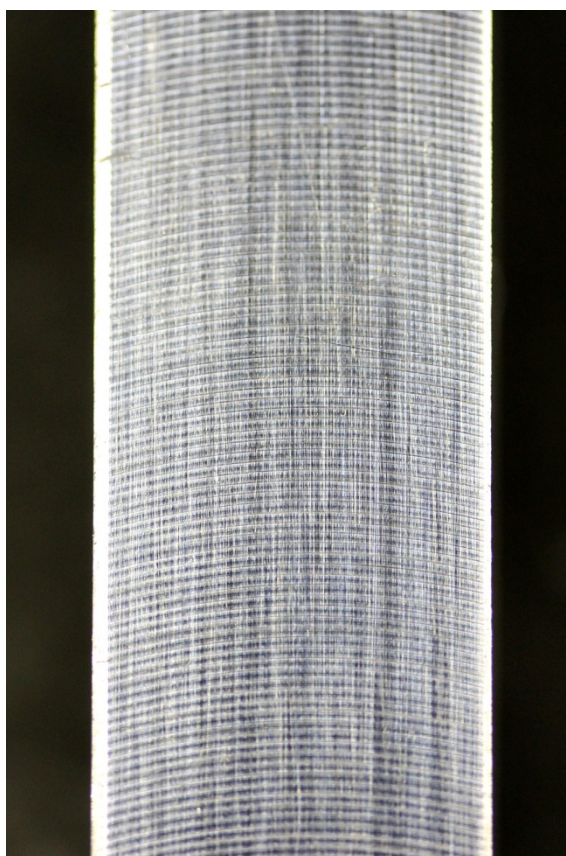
6 - Acabamento como recebido da usinagem mostrando marcas de fresa.
